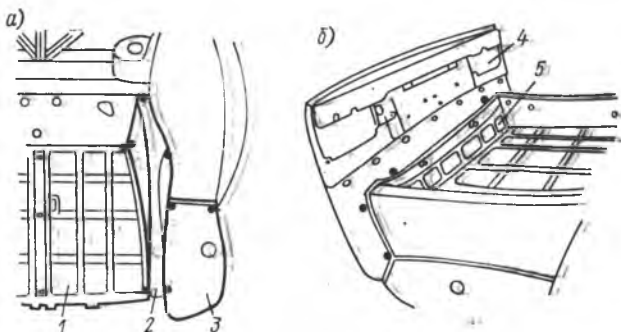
Сварка (прихватка) латунным припоем деталей задка кузова (точками обозначены места прихватки деталей)
